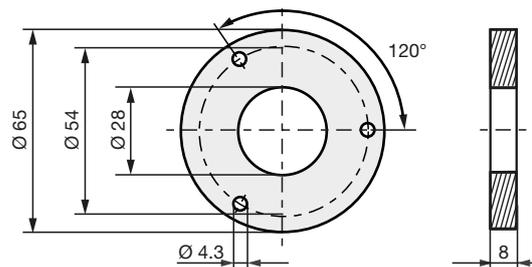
Accessori speciali BTL-P-1028-15R
